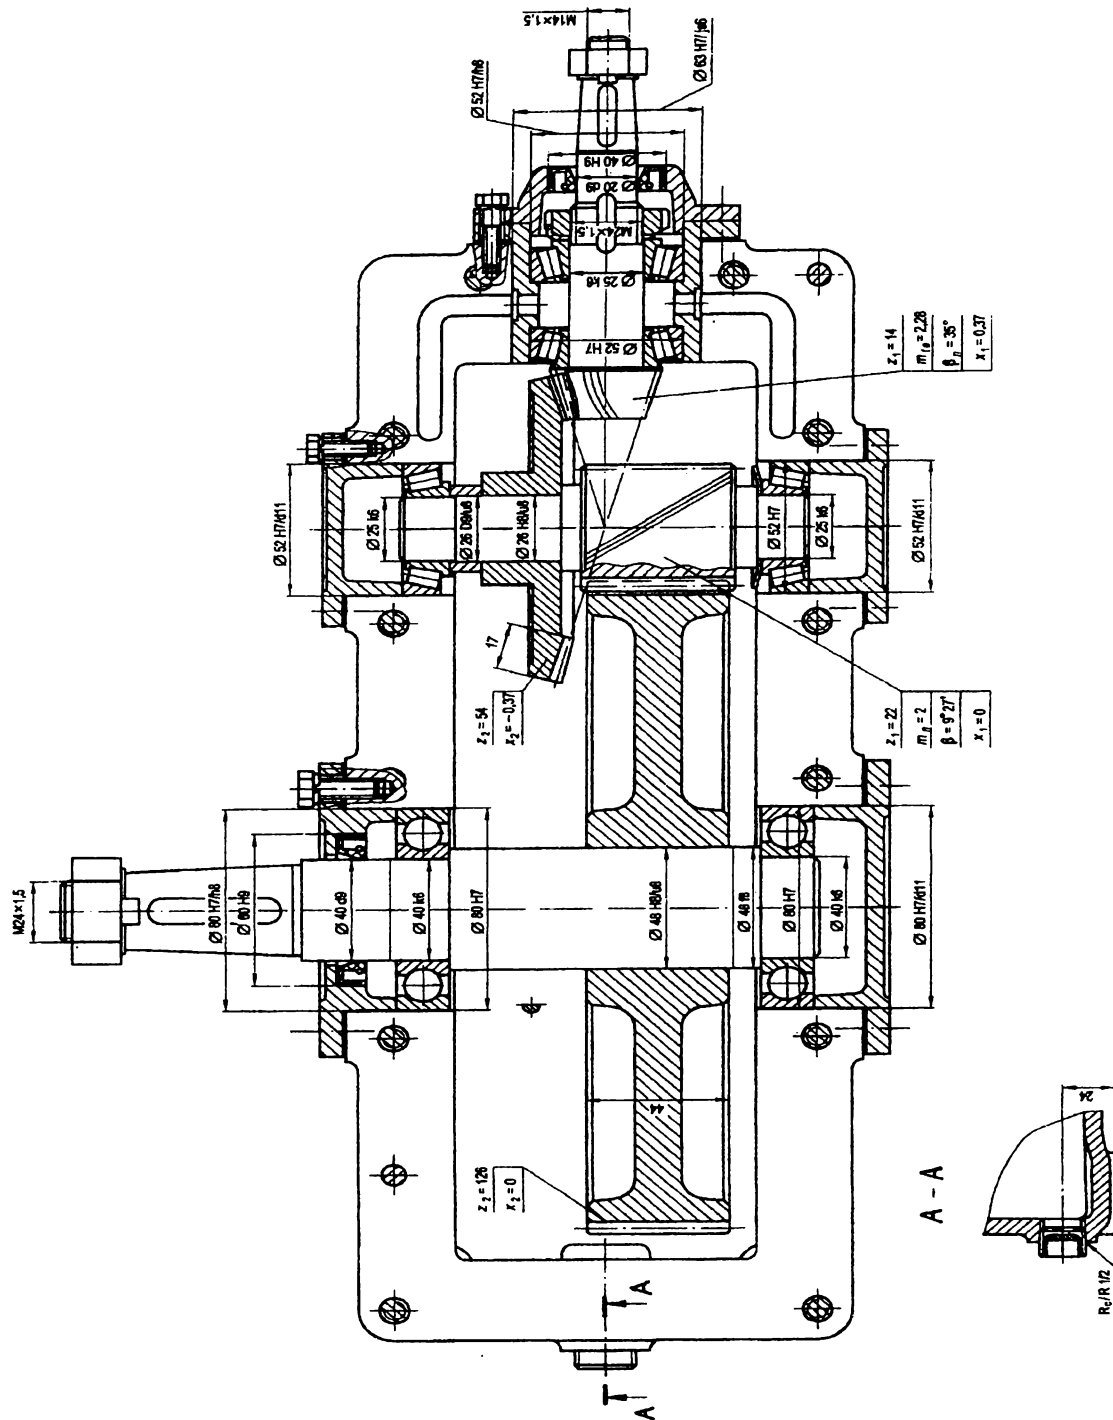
Редуктор коническо-цилиндрический горизонтальный с разъемом корпуса по осям валов
